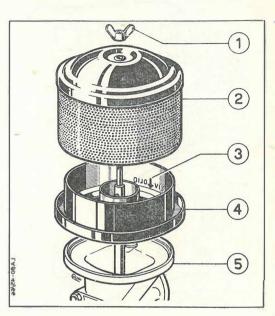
• SMONTAGGIO DEL FILTRO ARIA
